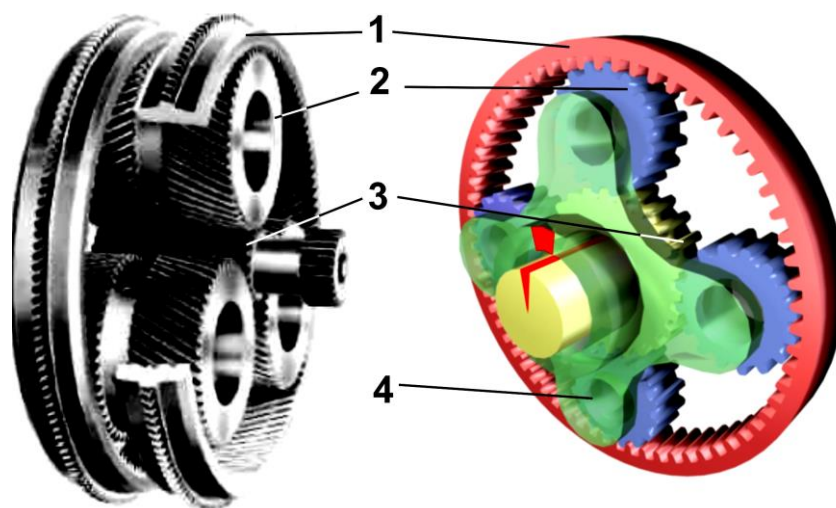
Конструктивні особливості планетарного редуктора:
